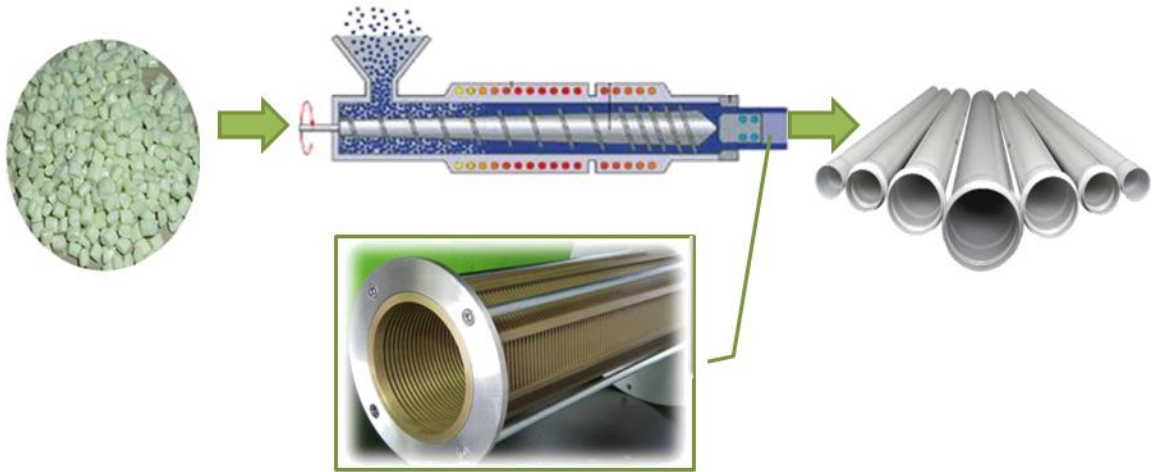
Processo de Moldagem de Tubos de Esgoto.
